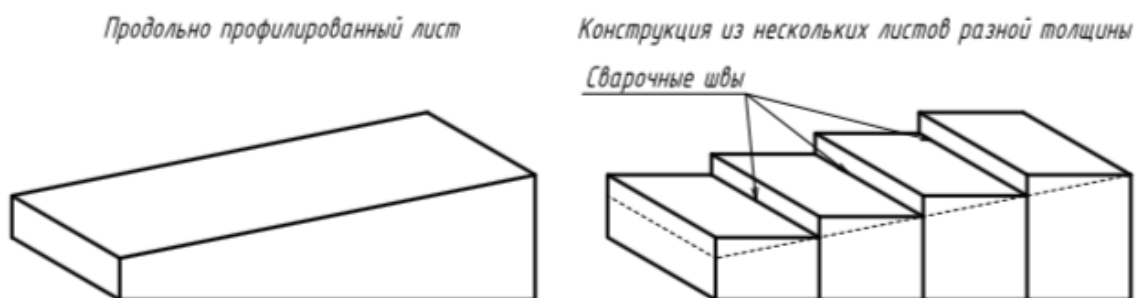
Сокращение длины сварных швов и уменьшения веса конструкции благодаря использованию разнотолщинных листов.
